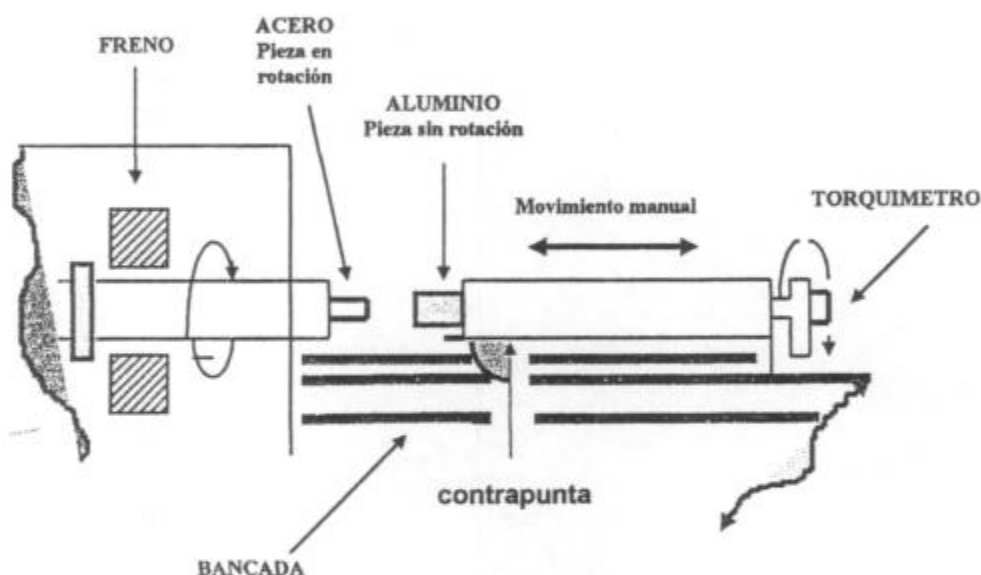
Esquema principal del equipo utilizado en la unión del acero/aluminio mediante la soldadura por fricción.
